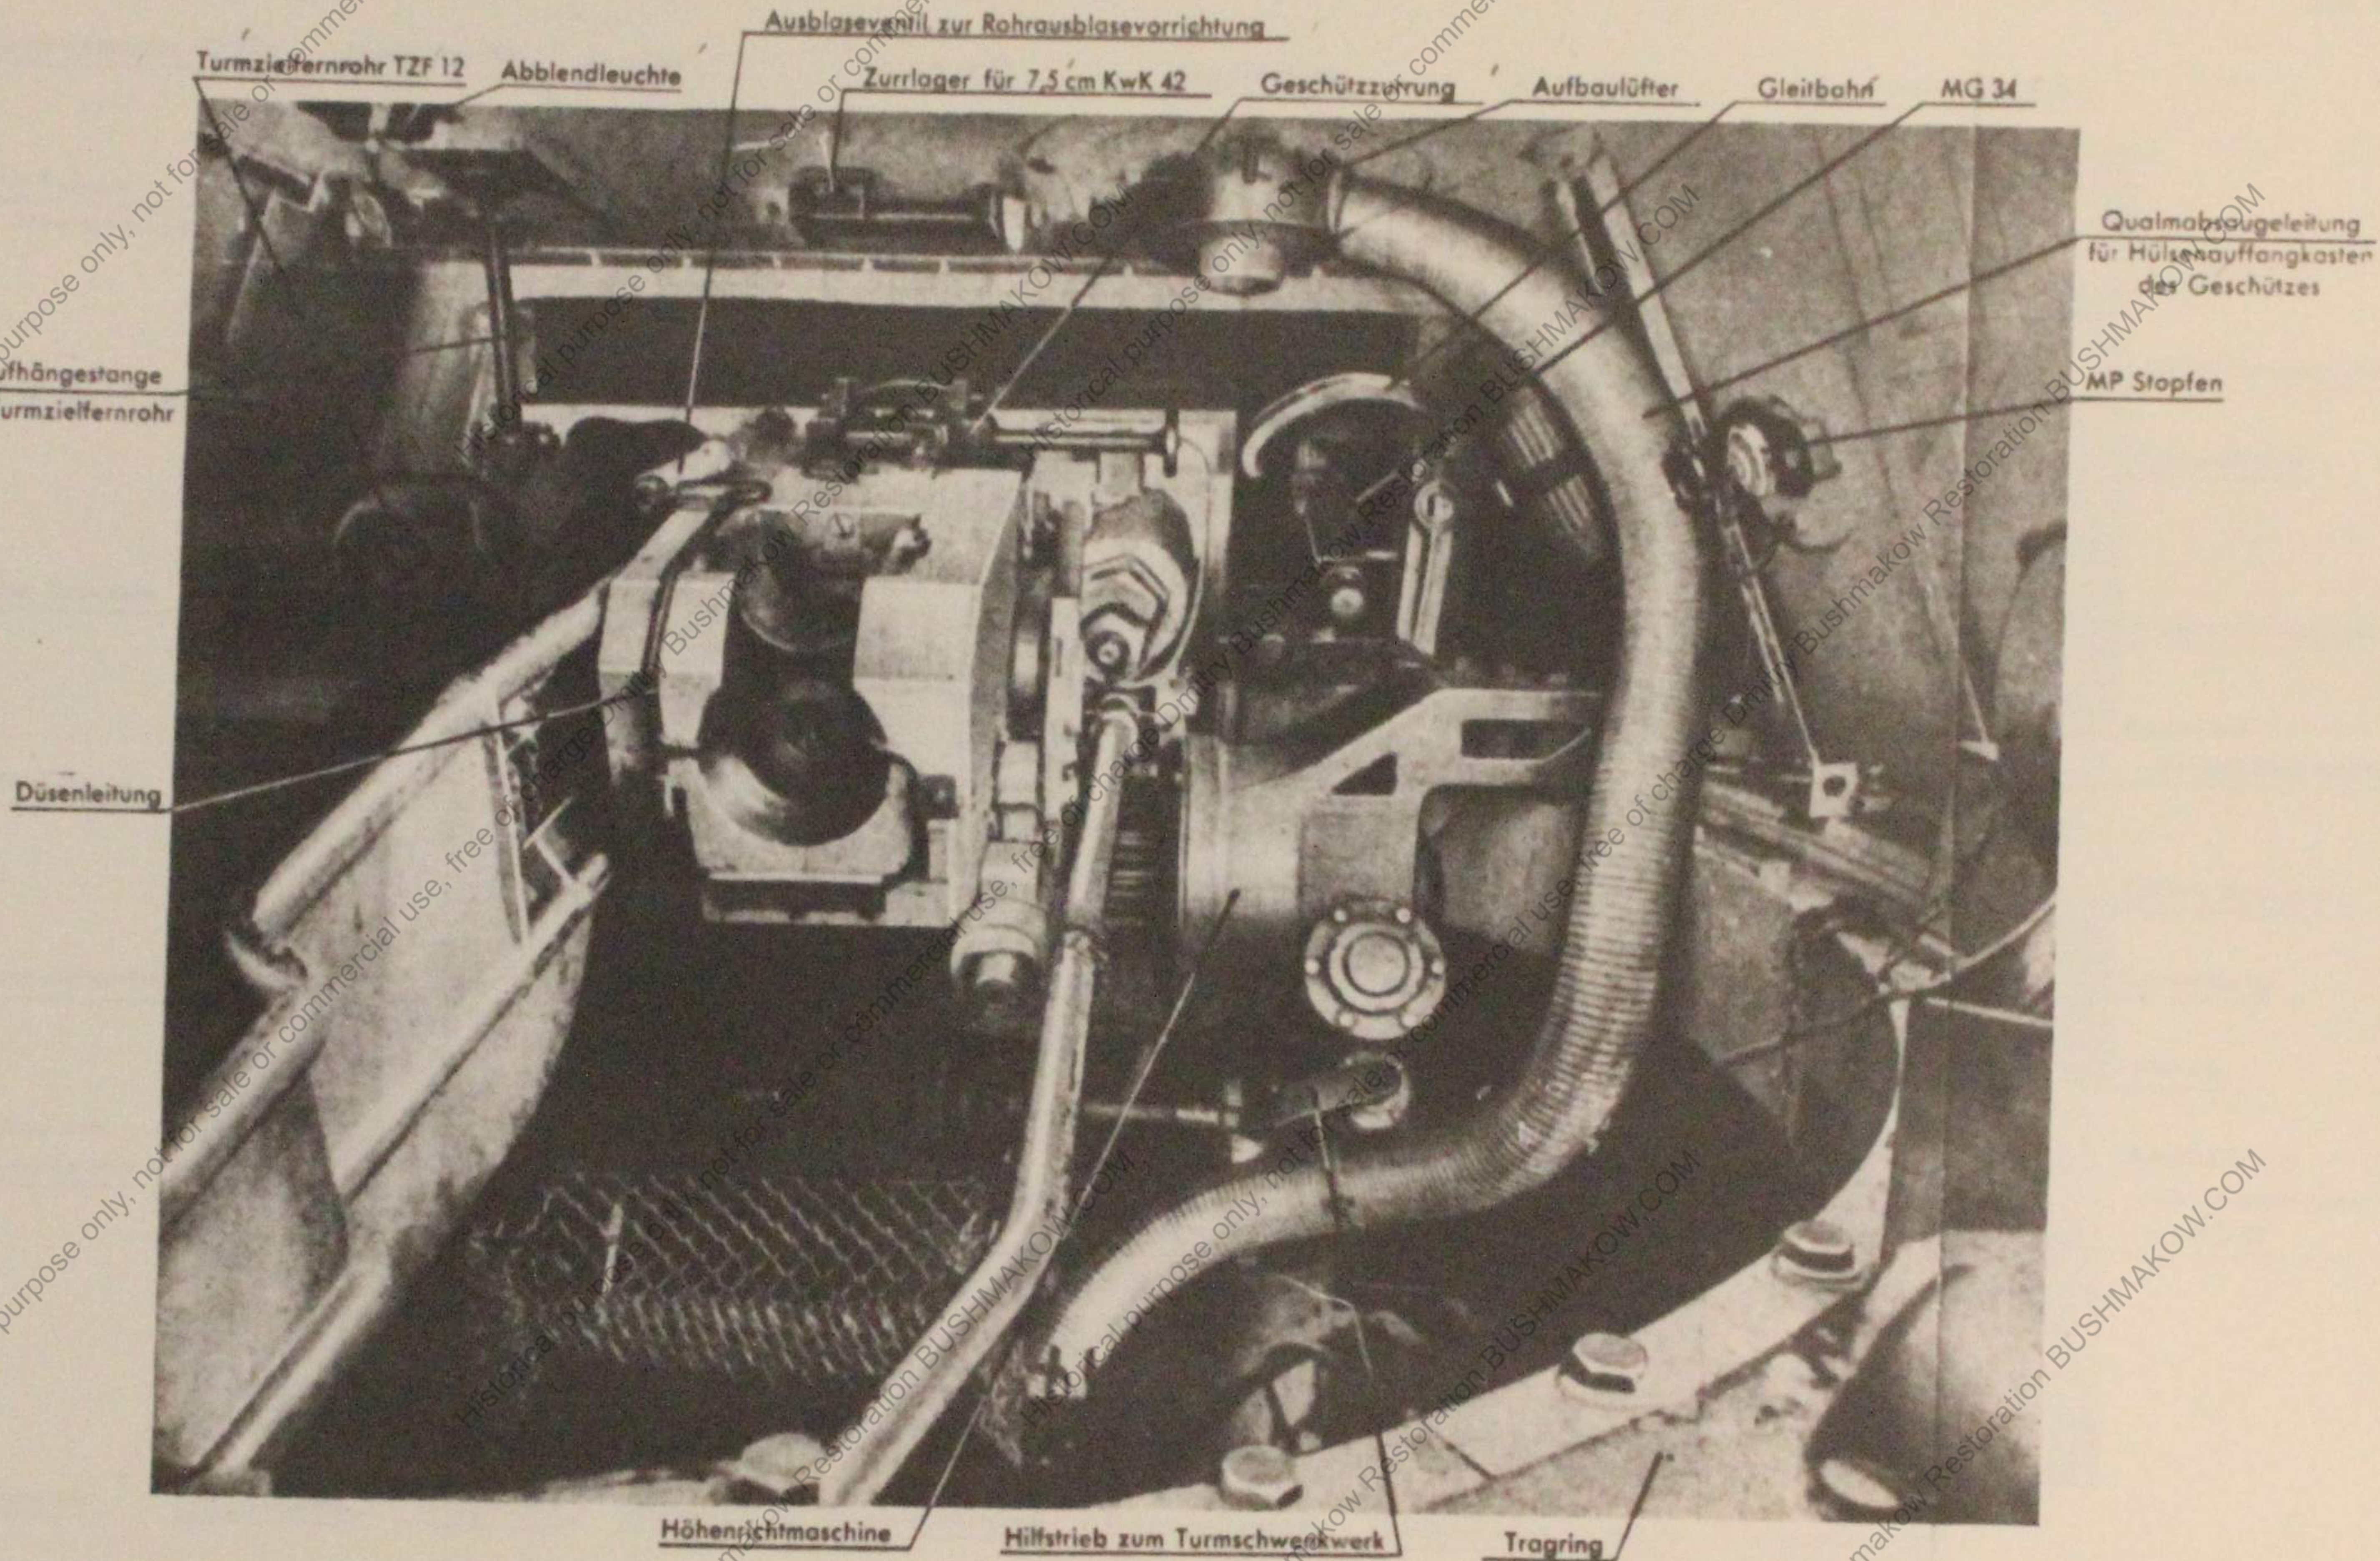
Turm, Pz Kpfw Panther, Ausf. D, Innenansicht, von hinten
